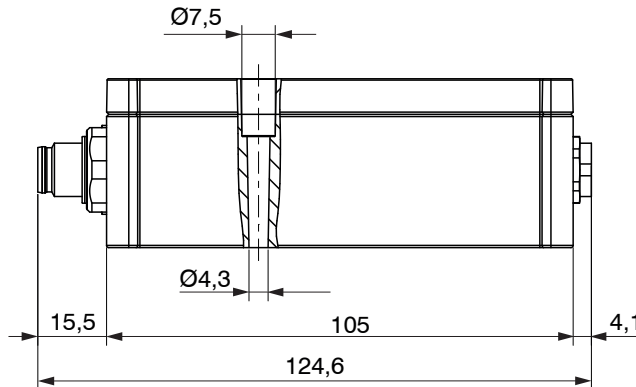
Maßzeichnung des Controllers MSC7802(010), Abmessungen in mm
